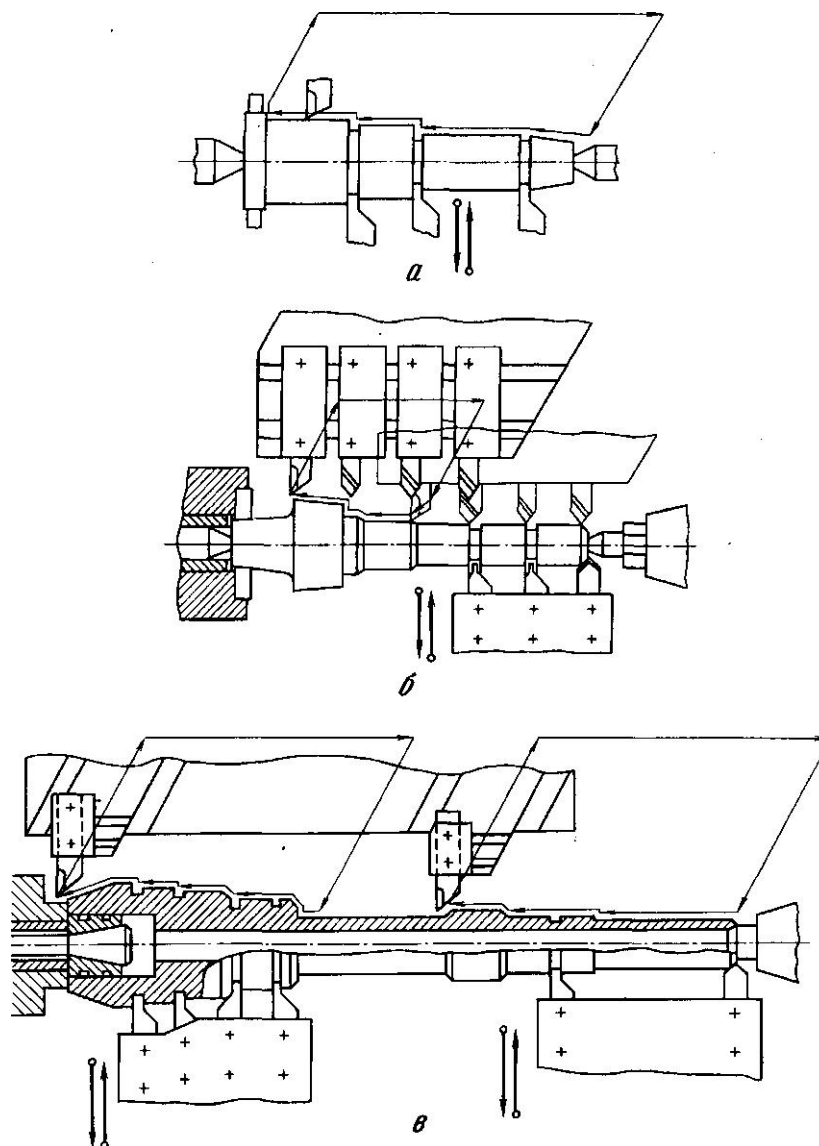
Схема обробки заготовок на багаторізцево-копіювальних напівавтоматах: а) одним різцем; б) блоком різців; в) з двох копіювальних супортів.
